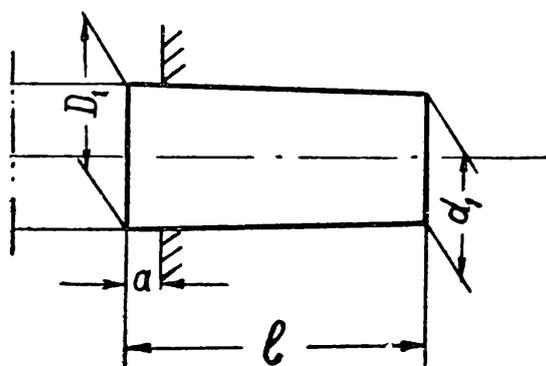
Размеры концов оправок для сверлильных патронов (укороченный конус Морзе).
